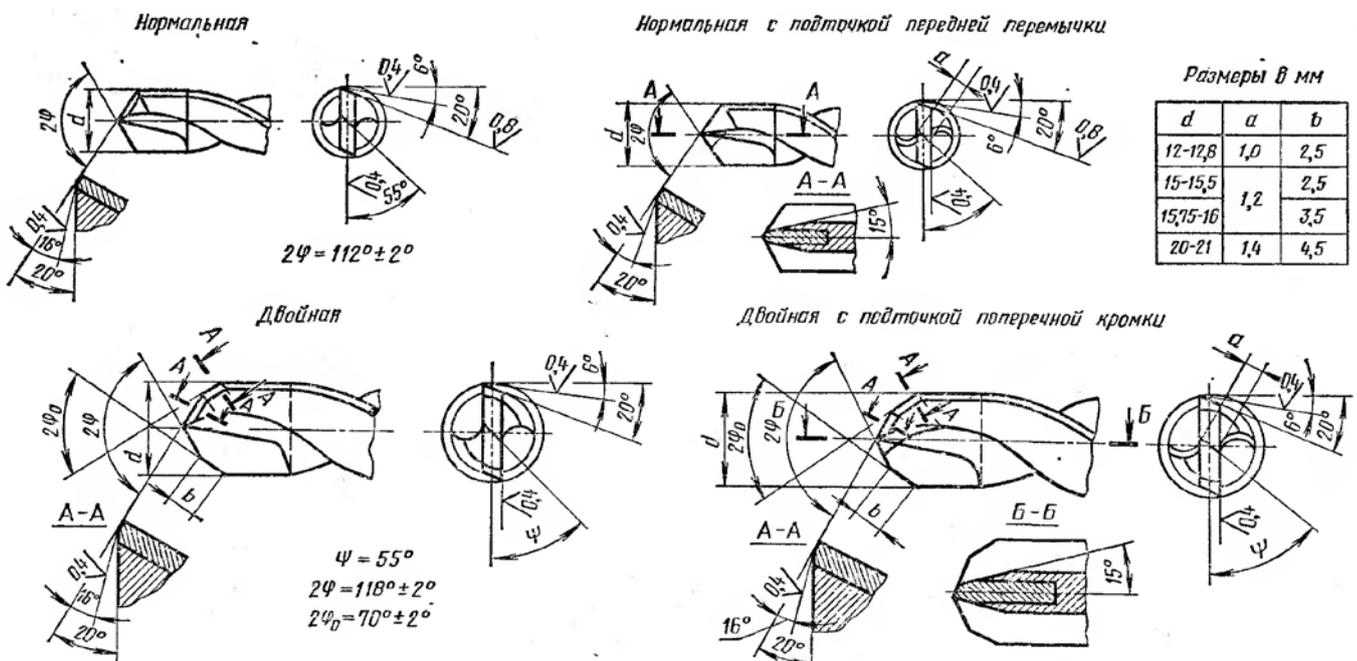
Формы заточки сверл с пластинками из твердого сплава
